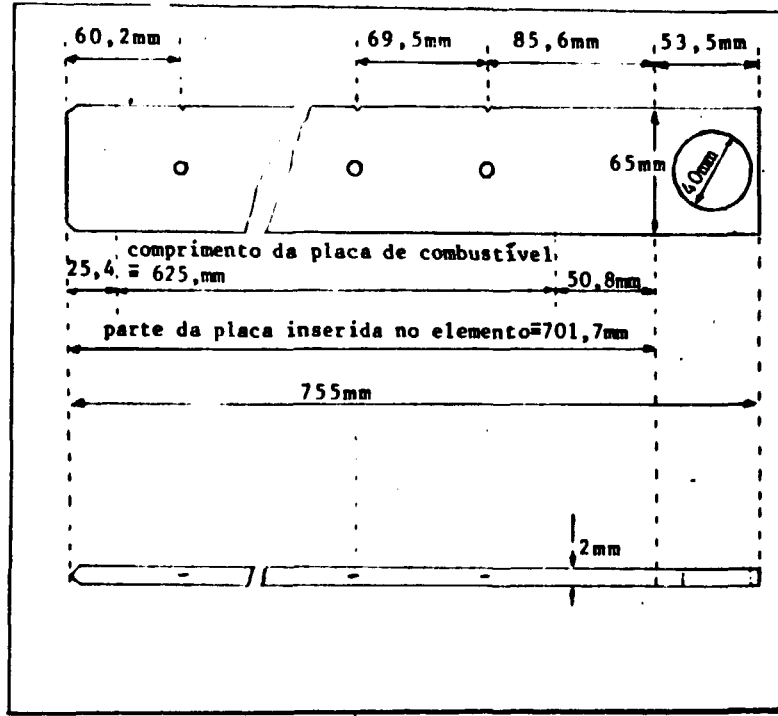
Esboço das Placas-Suporte de Folhas
